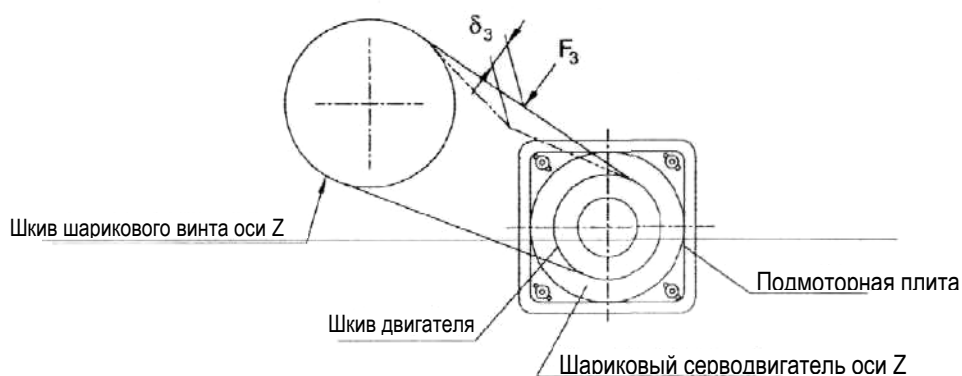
Зубчатый ремень привода для серводвигателя оси Z
